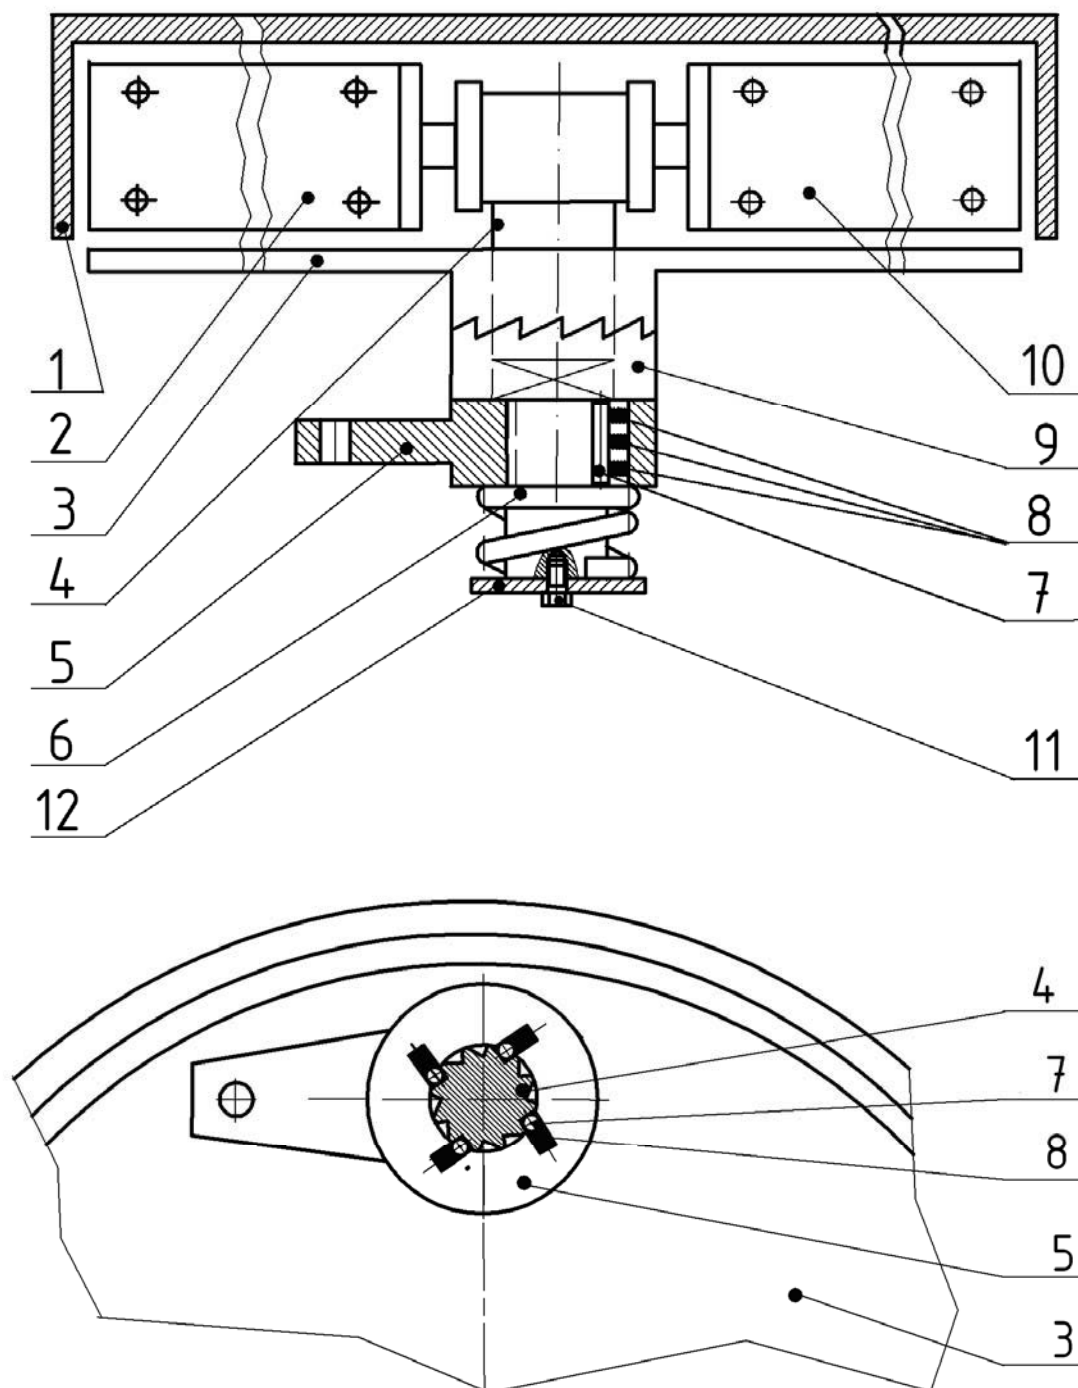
Автоматический регулятор зазора между тормозными колодками и тормозным барабаном колесного тормозного механизма [7]: 1 – барабан; 2 – колодка; 3 – щит тормозной; 4 – вал; 5 – рычаг; 6 – пружина; 7 – ролики; 8 – пружина; 9 – втулка; 10 – колодка; 11 – винт; 12 – шайба
